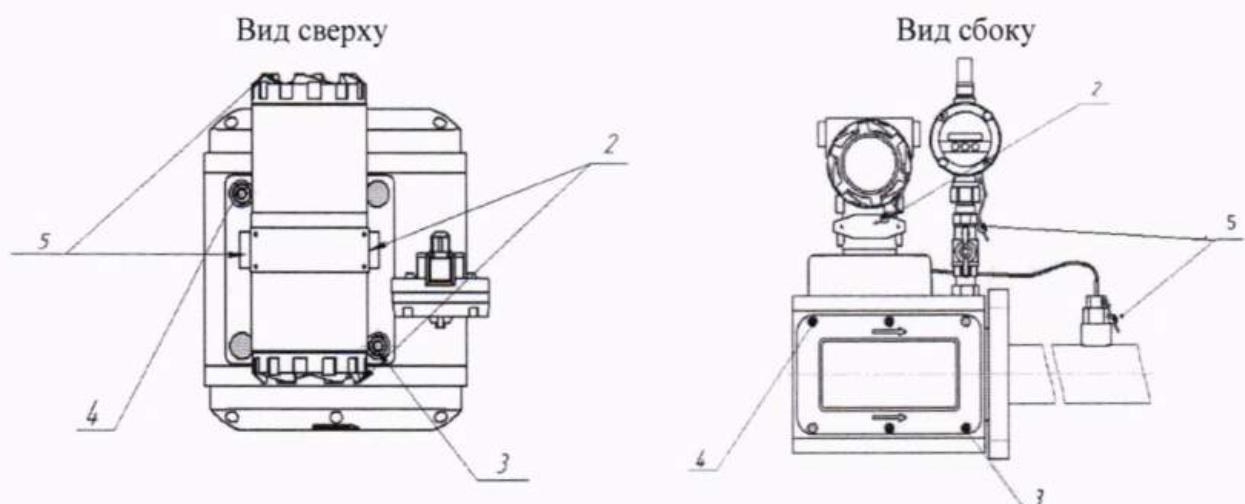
Корпус прямоугольного сечения с совмещенными защитными крышками
